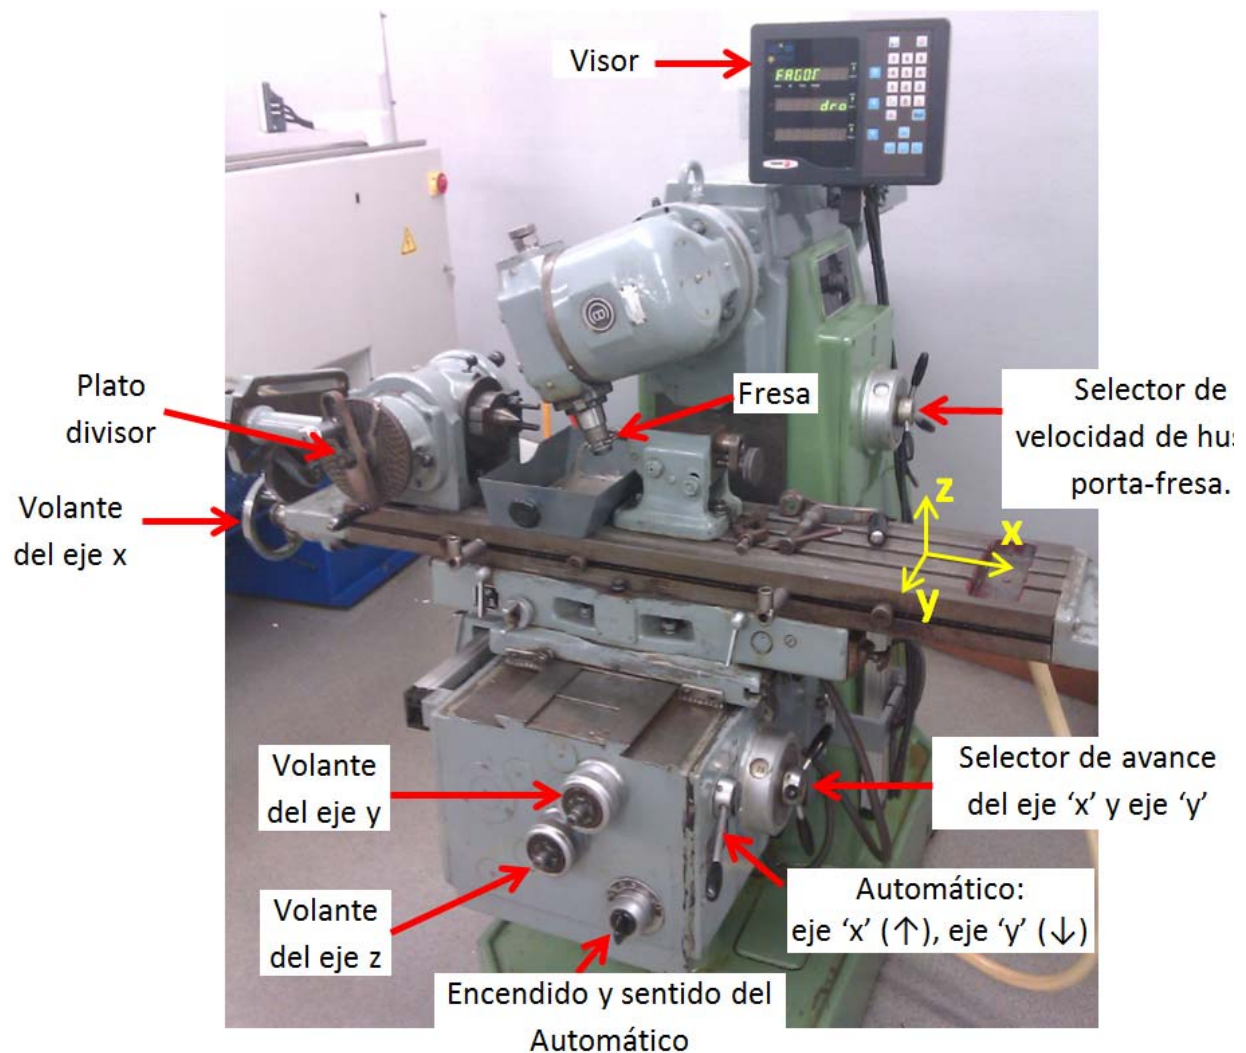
Máquina-herramienta fresadora del taller de fabricación para el mecanizado del piñón helicoidal.
